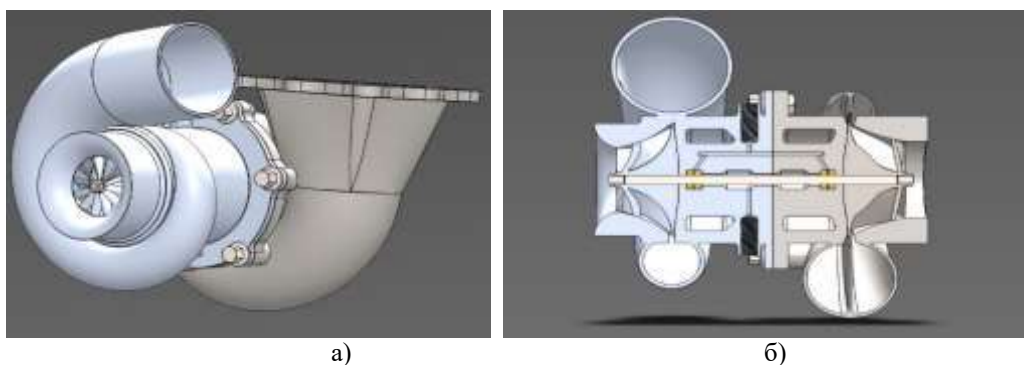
Разработанная 3-D модель турбокомпрессора ТКР-7С-6М автомобиля КамАЗ 740.602: а) общий вид; б) разрез турбокомпрессора
